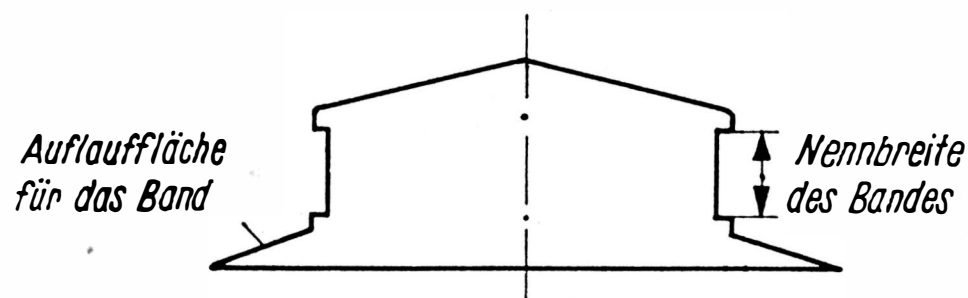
Führungsrolle mit Auflaufläche für das Magnetband
